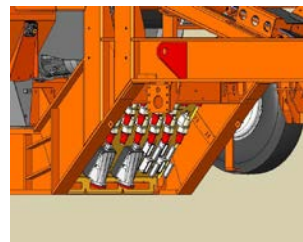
Retirada da tampa de proteção das tomadas / Removal of protection cover of sockets
